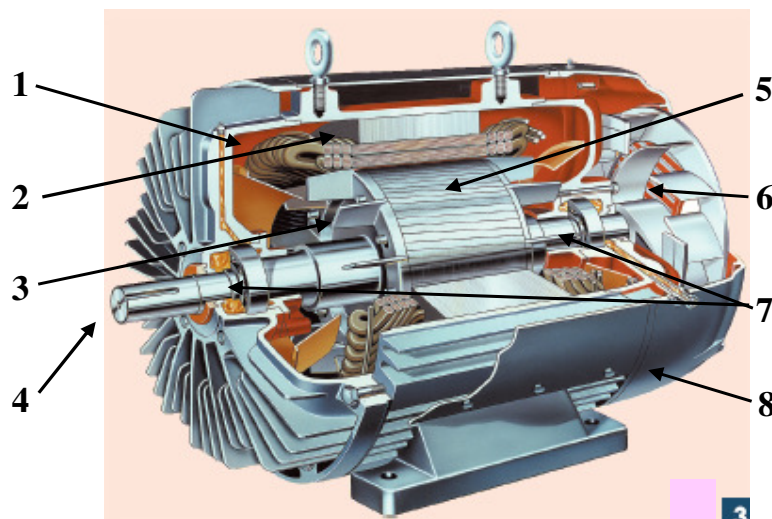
Motor de Indução com rotor em gaiola [9].
